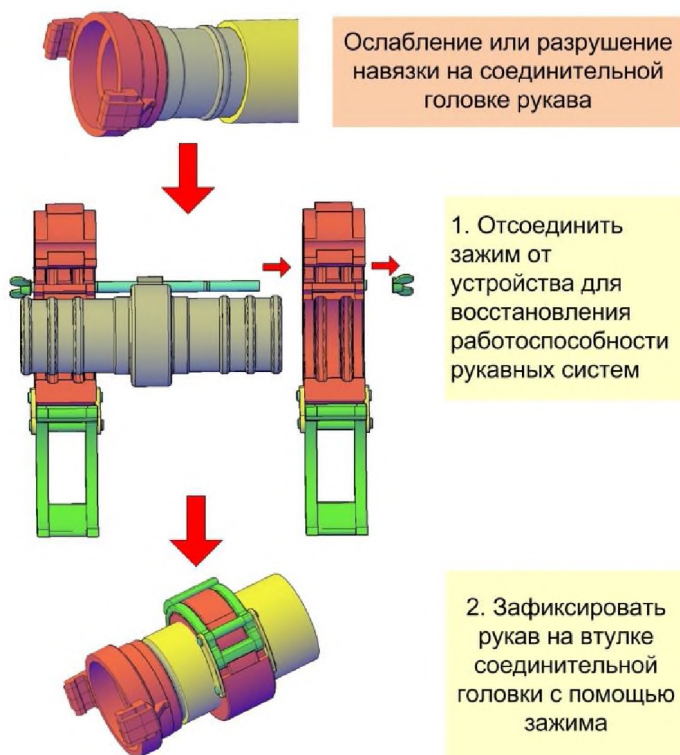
Порядок закрепления напорного рукава на втулке соединительной головки
